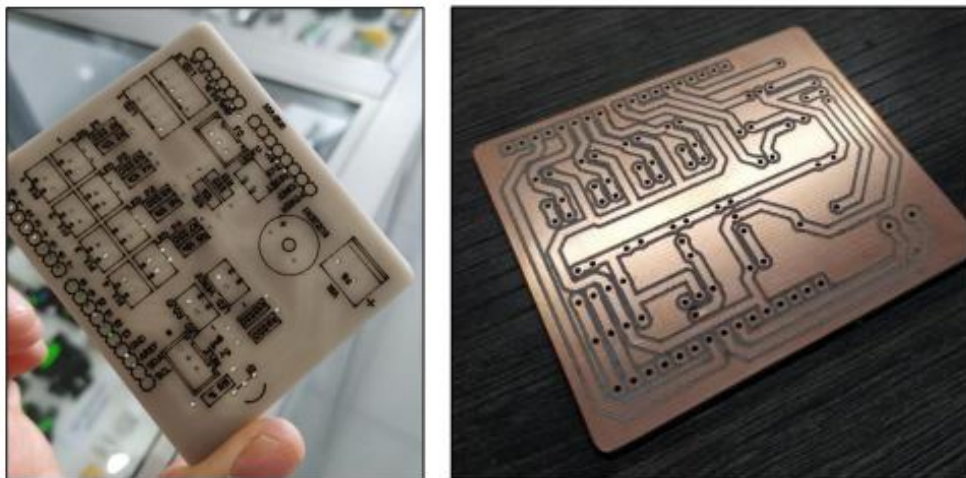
Parte superior y posterior de la PCB sin componentes soldados.
